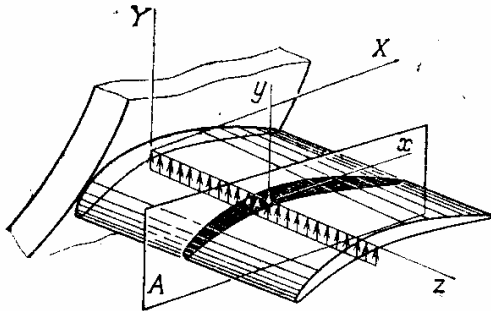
Лопатка компрессора под действием изгибающей нагрузки
